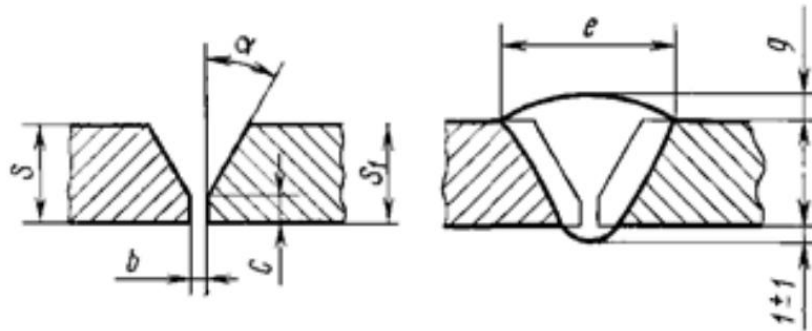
Ескіз зварного з'єднання С17 згідно ГОСТ 14771-76
